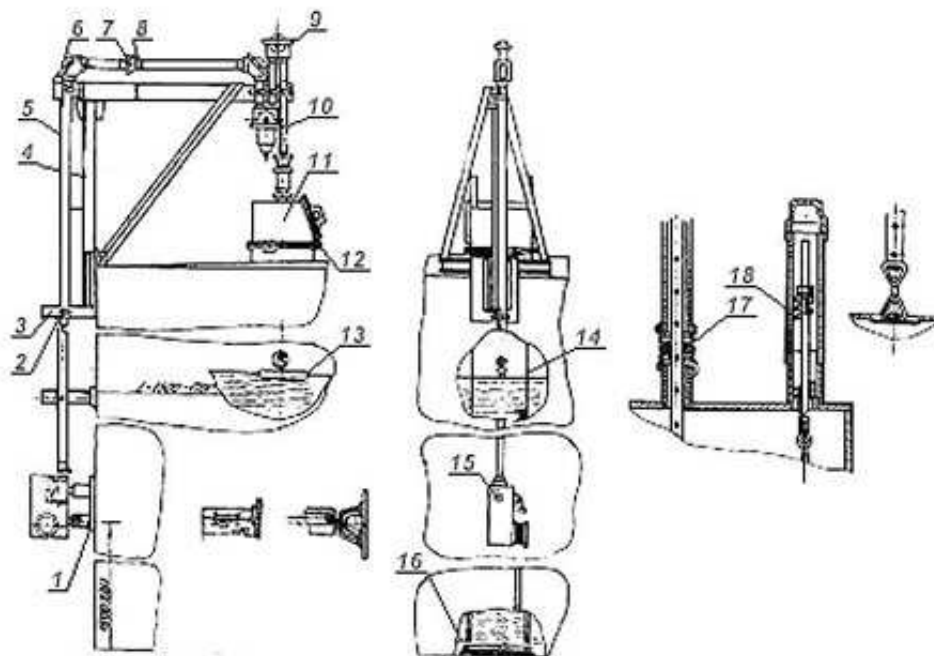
Компоновка и кинематическая связь частей уровнемера на вертикальном наземном цилиндрическом резервуаре
